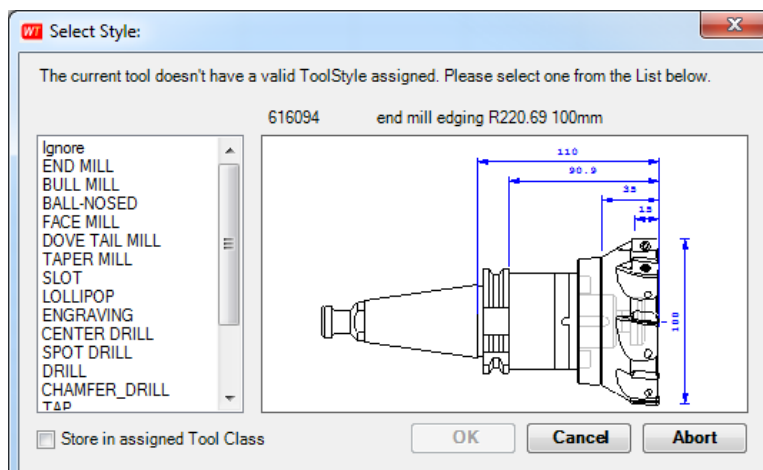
Zuordnung Komplett-Werkzeug zu SolidCam Werkzeugtyp
